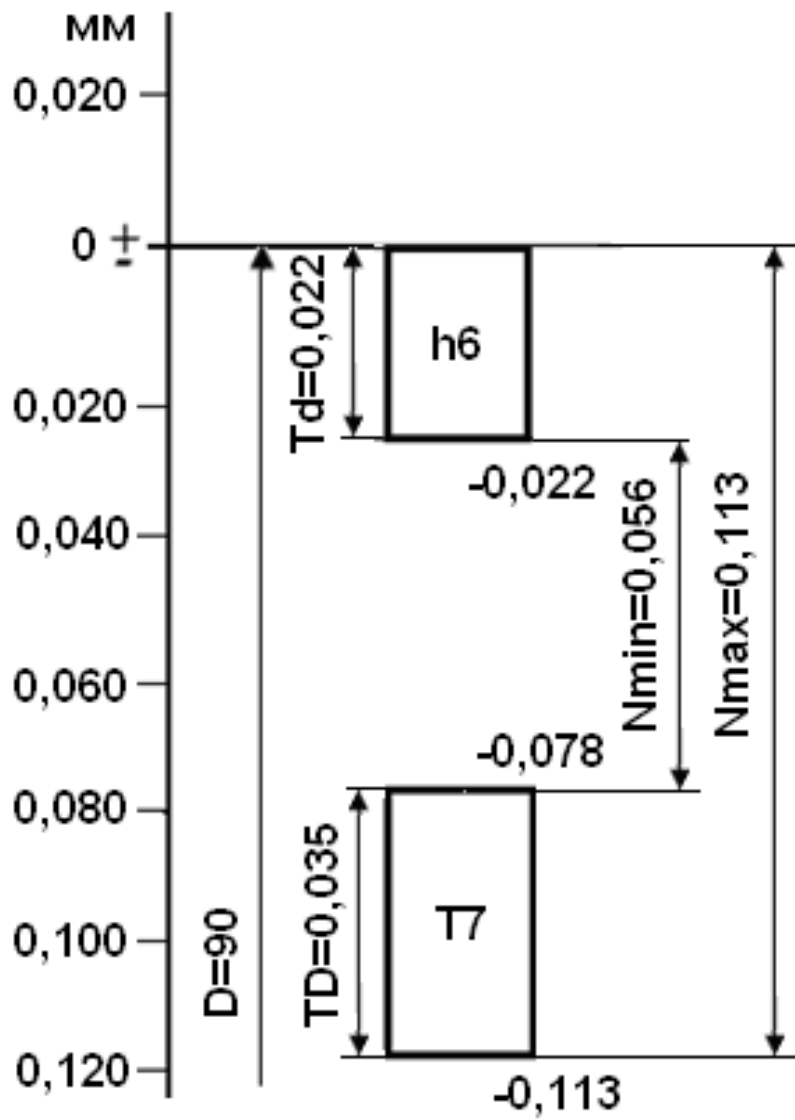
Схема розташування полів допусків деталей з'єднання $\varnothing 90T7/h6$
